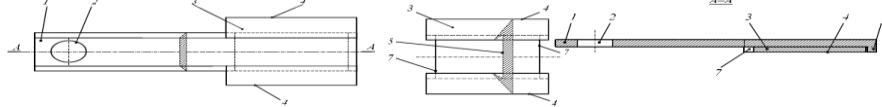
Ніж роторної косарки з рухомою ріжучою накладкою
